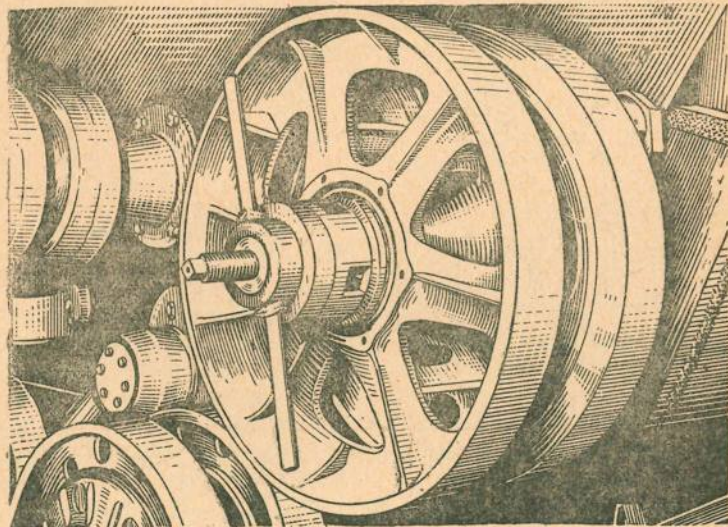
Запрессовка направляющего колеса на ось кривошипа при помощи приспособления
